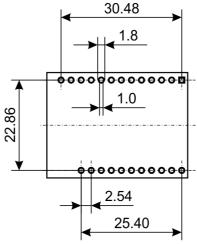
THT Footprint [mm] – Vista desde arriba
